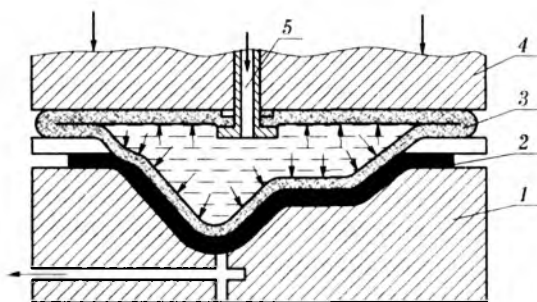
Схема штамповки детали с помощью жидкости:
